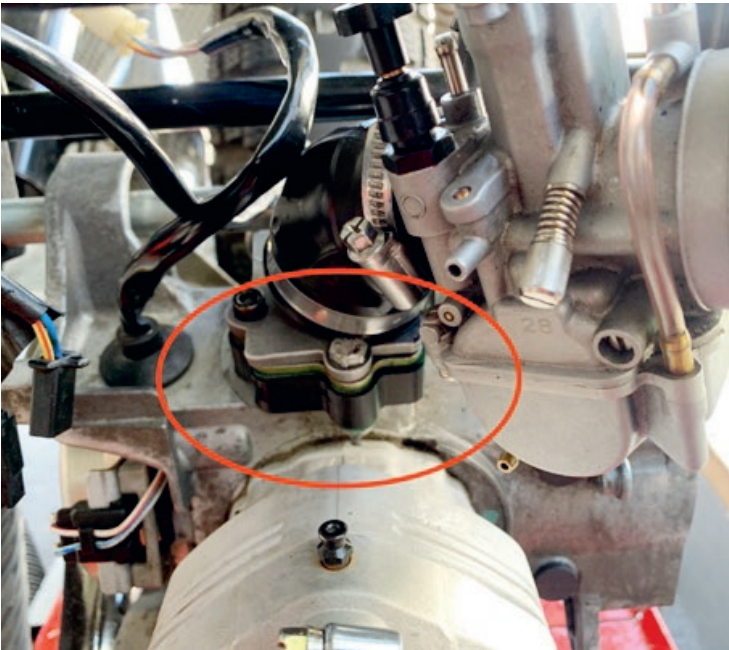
Membranblock-Spacer im Motor eingebaut
